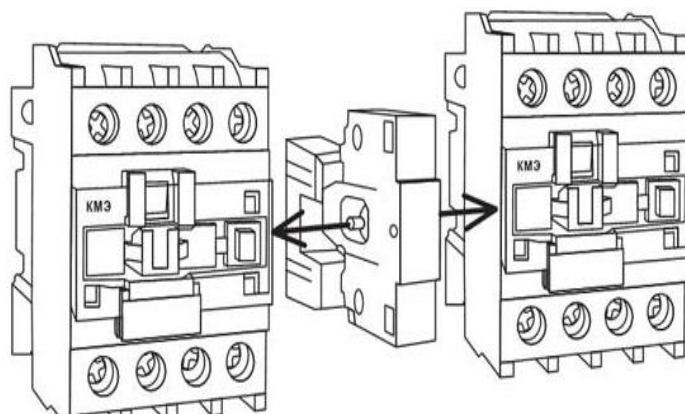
Реверсивный магнитный пускатель с механической блокировкой
